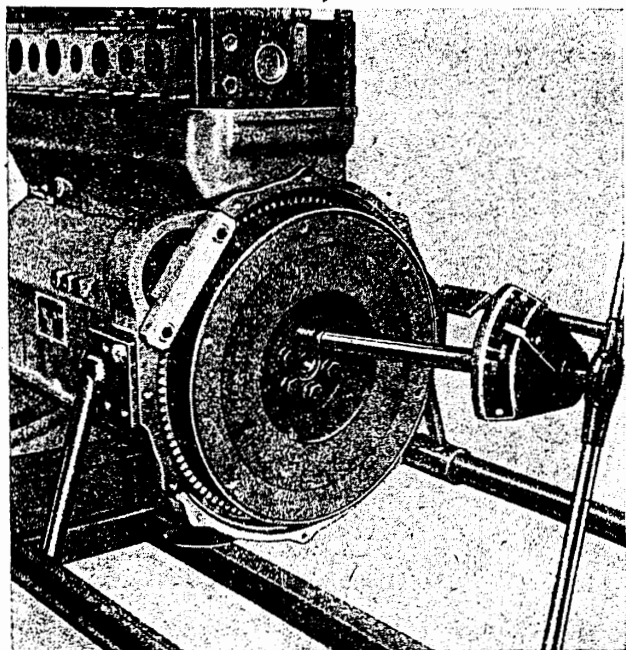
Befestigungsschrauben des Schwungrades mit Drehmomentschlüssel 100 ... 105 Nm (10 ... 10,5 kpm) anziehen, dabei mit Arretierung (Werkzeug Nr. 324.020-M 114) Motor feststellen
